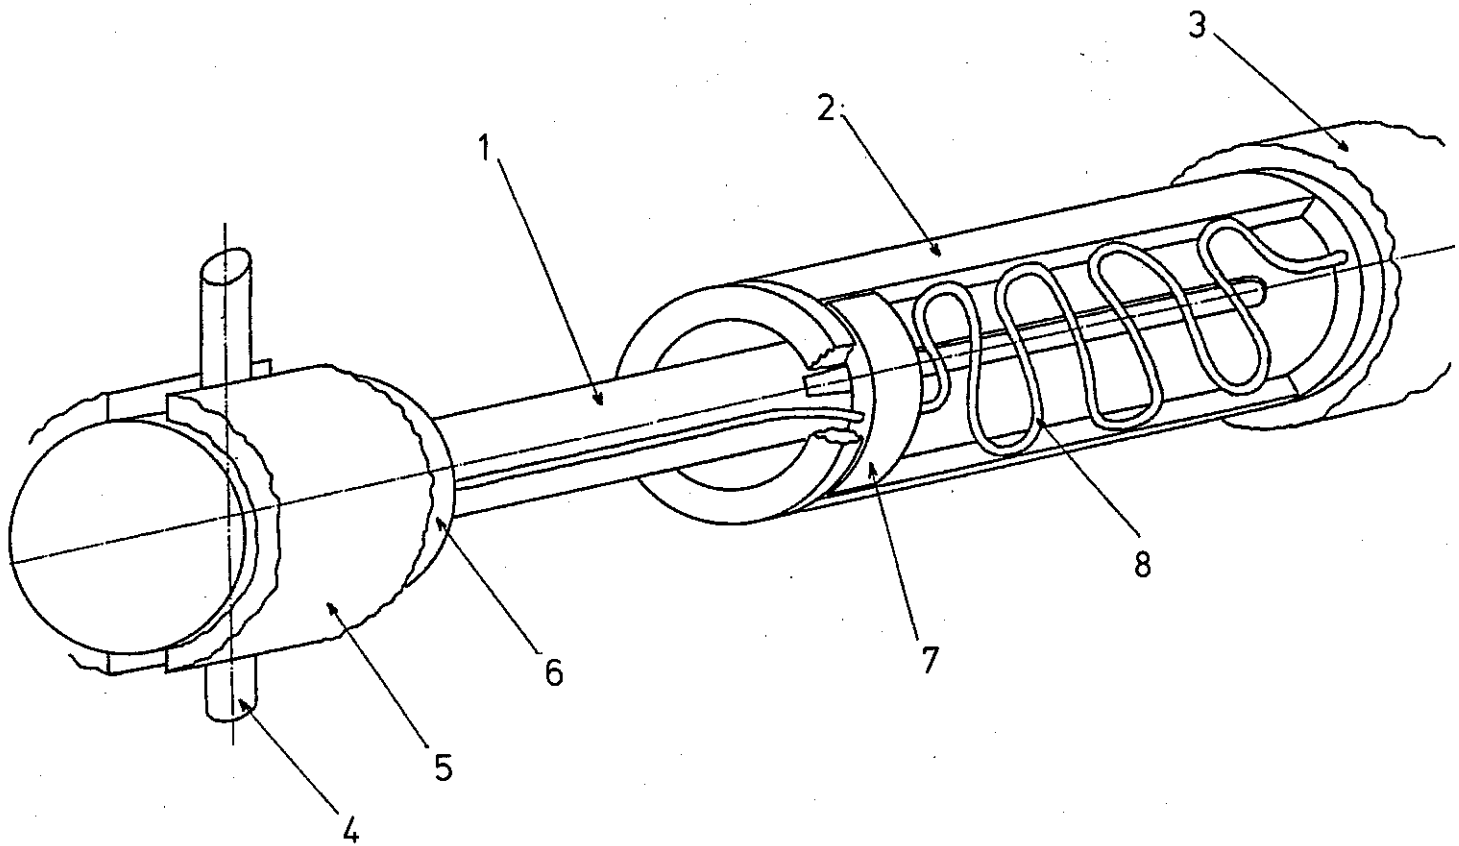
MECANISME ASSURANT LE MOUVEMENT AXIAL DE LA SONDE
